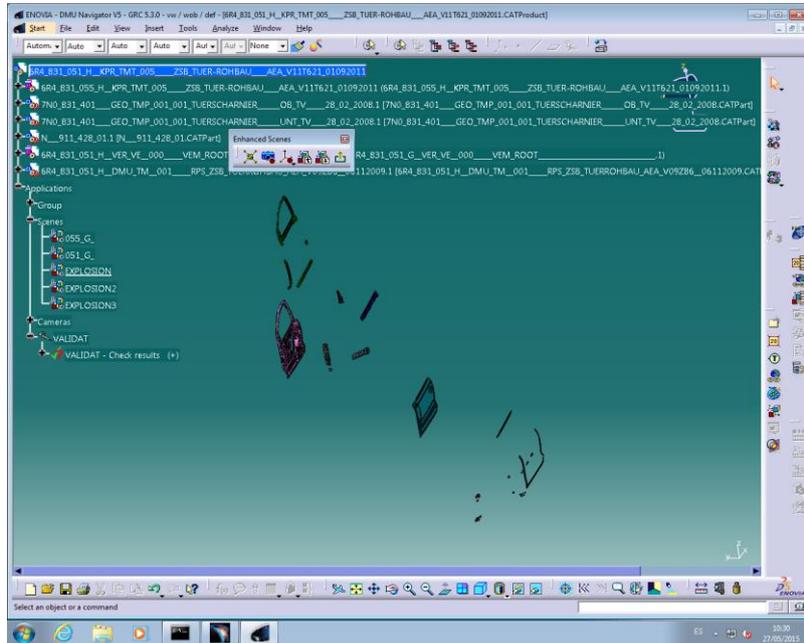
Explosionado completo del conjunto puerta anterior izquierda en DMU
